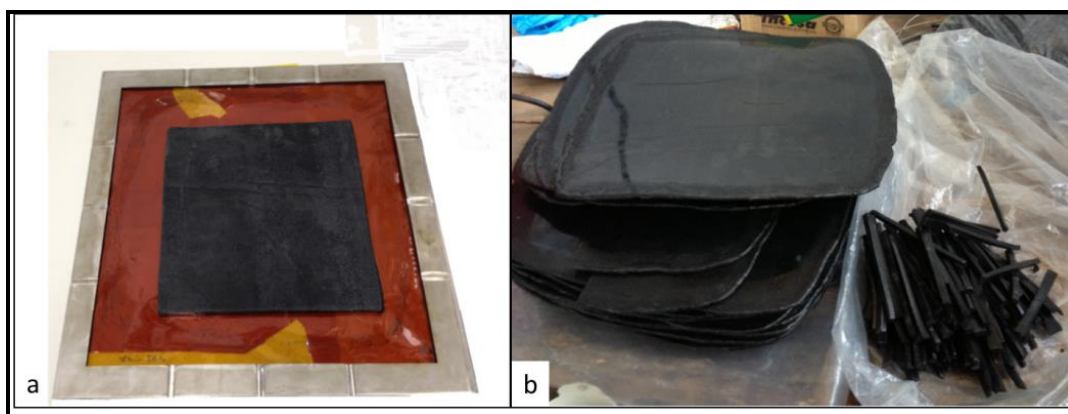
Molde com placa a ser vulcanizada (a) e placas vulcanizadas (b).
